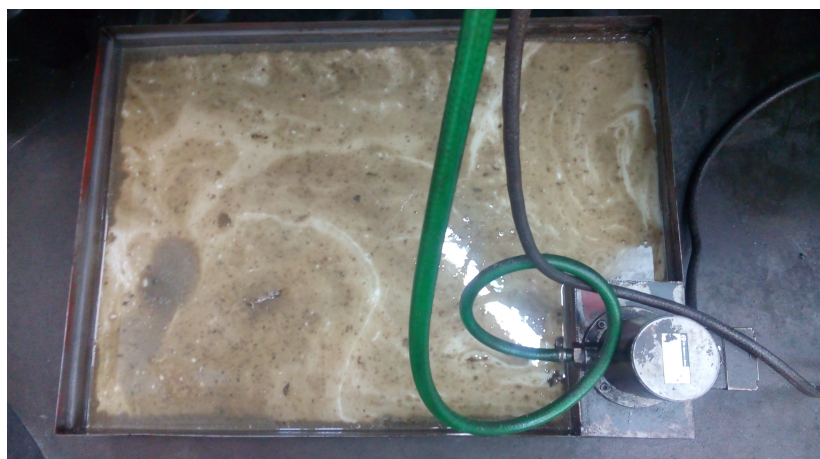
Externí nádrž chladicí kapaliny (soustruh OPTIMUM)
